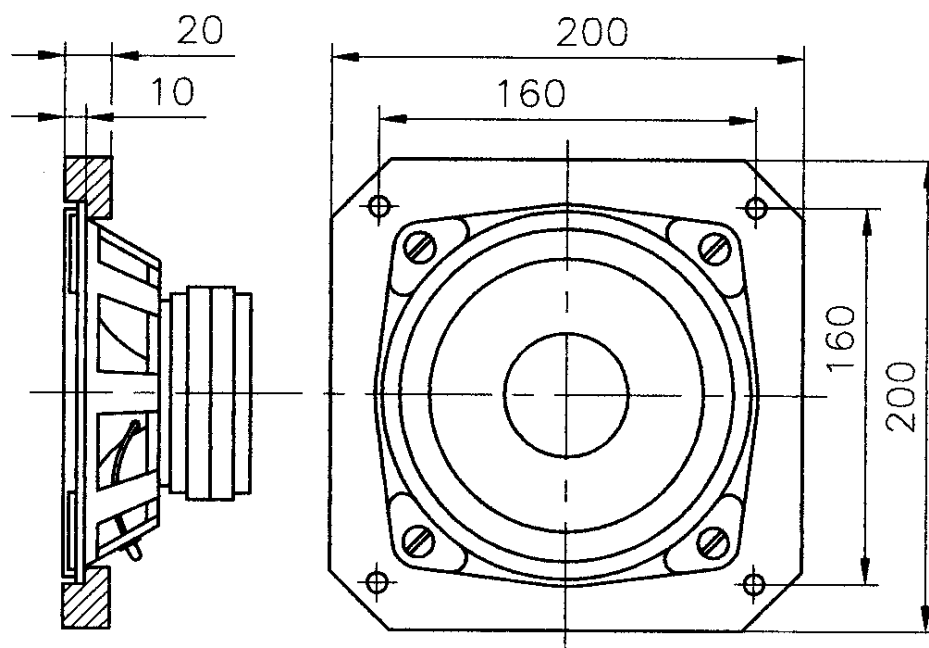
Общий вид фланца-переходника, для установки динамика 25ГДН-4-4.
